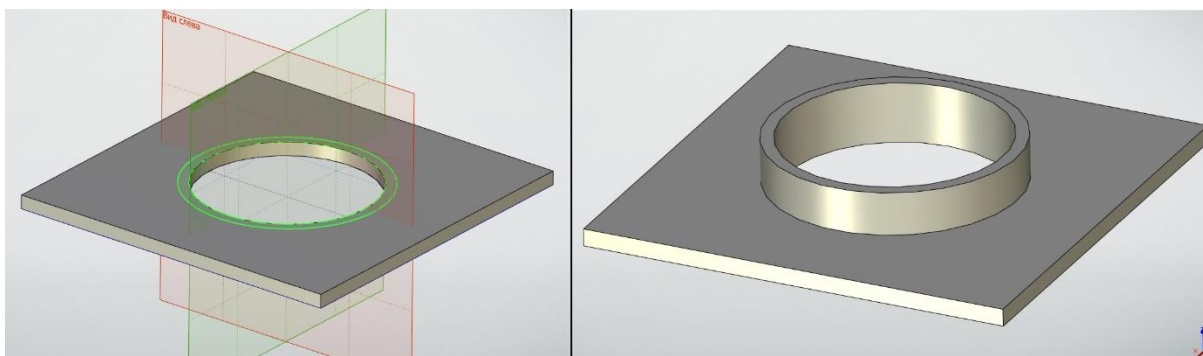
3D модель верхней пластины корпуса опорно-поворотного устройства
